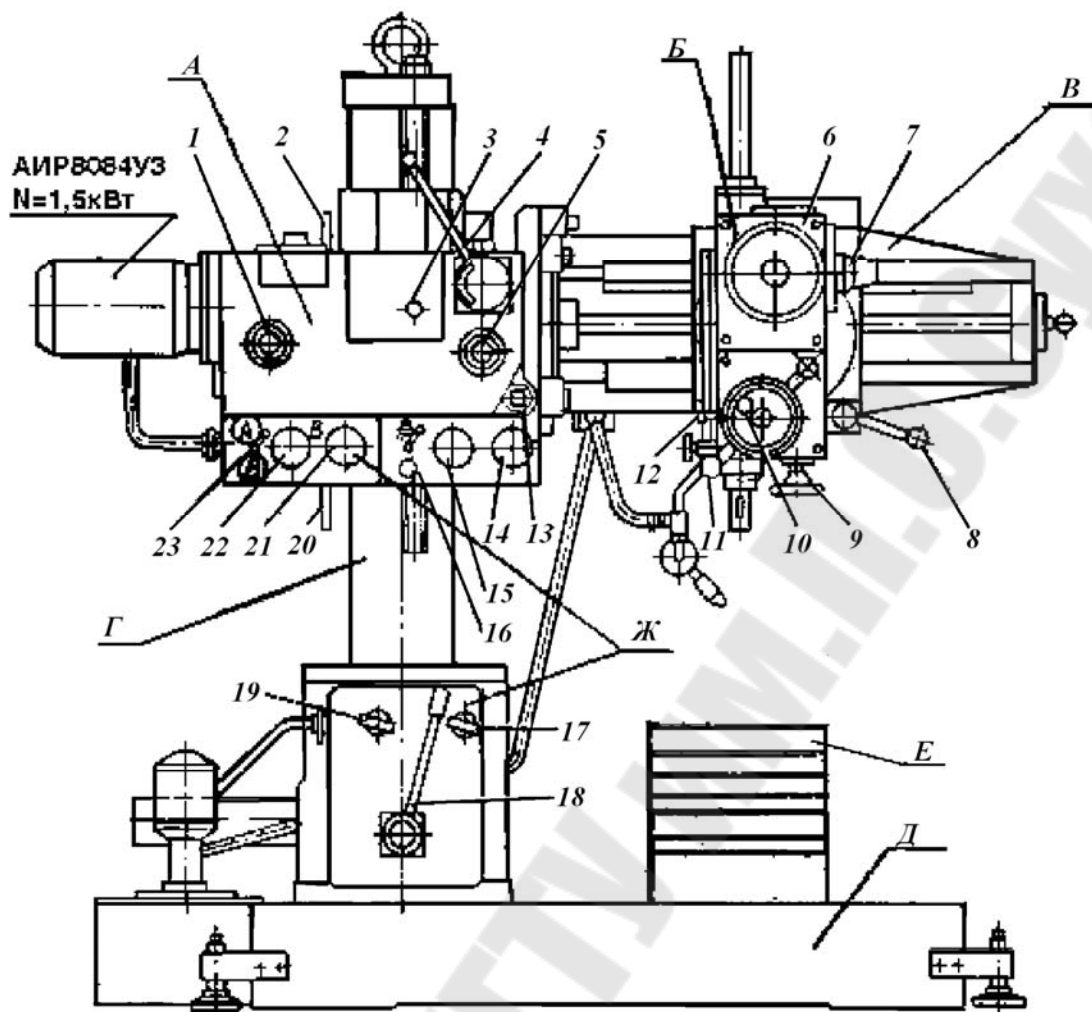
Эскиз общего вида станка с основными органами управления
